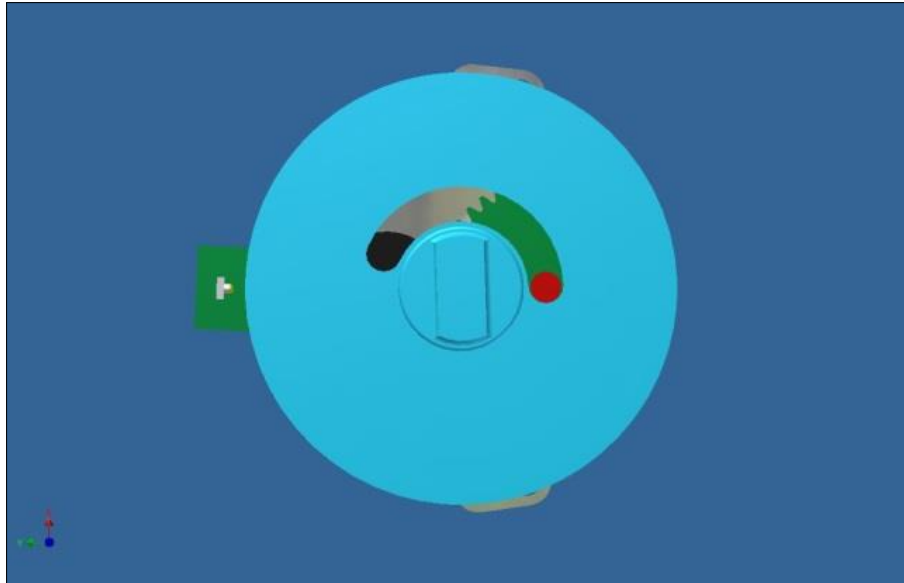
Primo stopping point e vista in pianta dell'incavatura
